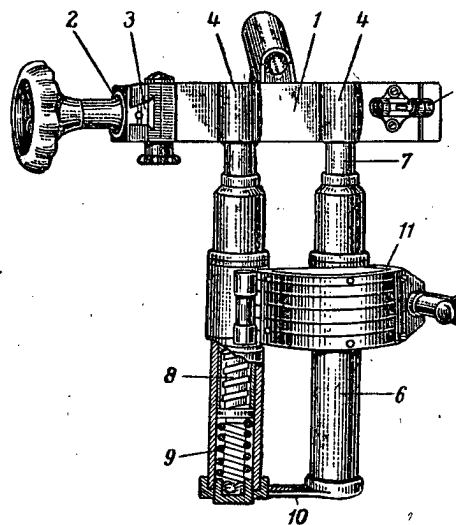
Вертлюг с амортизатором: 1 — корпус вертлюга; 2 — проушина; 3 — паз для крепления кронштейна; 4 — отверстие для штока; 5 — поперечный уровень; 6 — цилиндр амортизатора; 7 — шток; 8 — большая пружина; 9 — малая пружина; 10 — крышка цилиндра; 11 — обойма с наметкой
